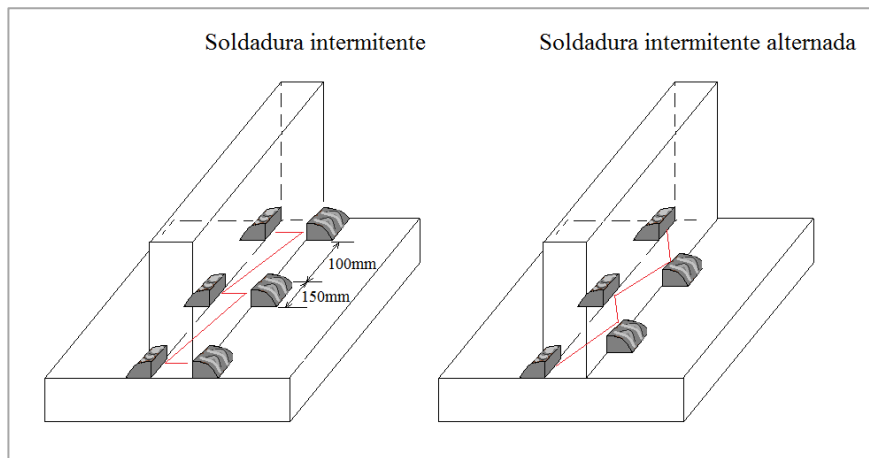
Diferentes métodos de soldadura intermitente em soldaduras de canto (fonte: West-sea)
